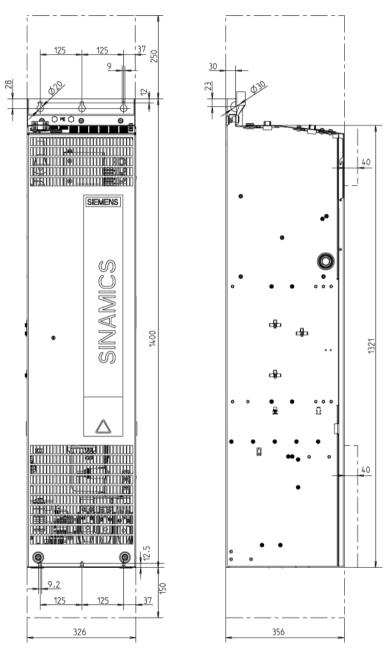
Габаритный чертеж модуля двигателя, типоразмер FX. Вид спереди, вид сбоку
